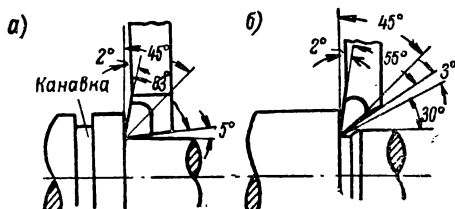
Формы поверхностей деталей, обрабатываемых с помощью гидросуппорта.
